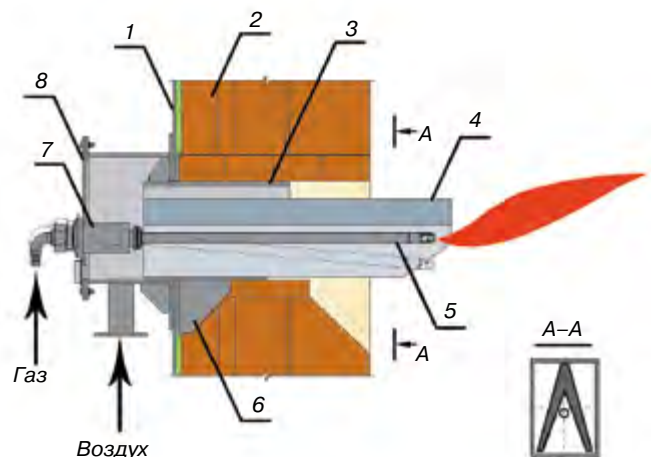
Периферийная горелка: 1 – кожух печи; 2 – футеровка; 3 – короб внутренний; 4 – фурма защитная; 5 – горелочная труба; 6 – ребра жесткости; 7 – поворотное устройство; 8 – фланец лицевой
